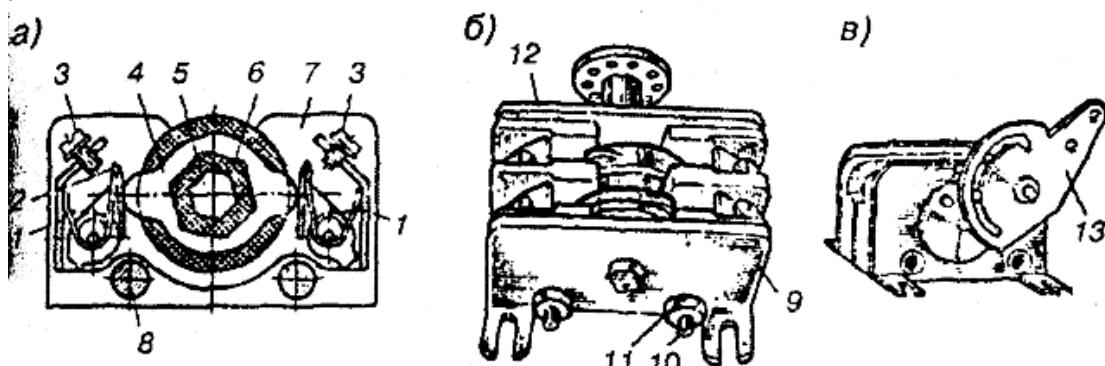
Блок-контакты приводов выключателей: а — конструкция КСА; б — внешний вид КСА; в — внешний вид КСУ
